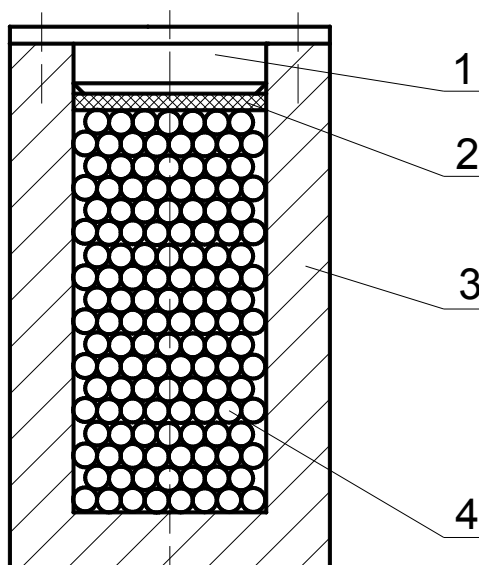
Схема бабы с наполнителем: 1 – крышка; 2 – упругая прокладка; 3 – корпус; 4 – шарики
